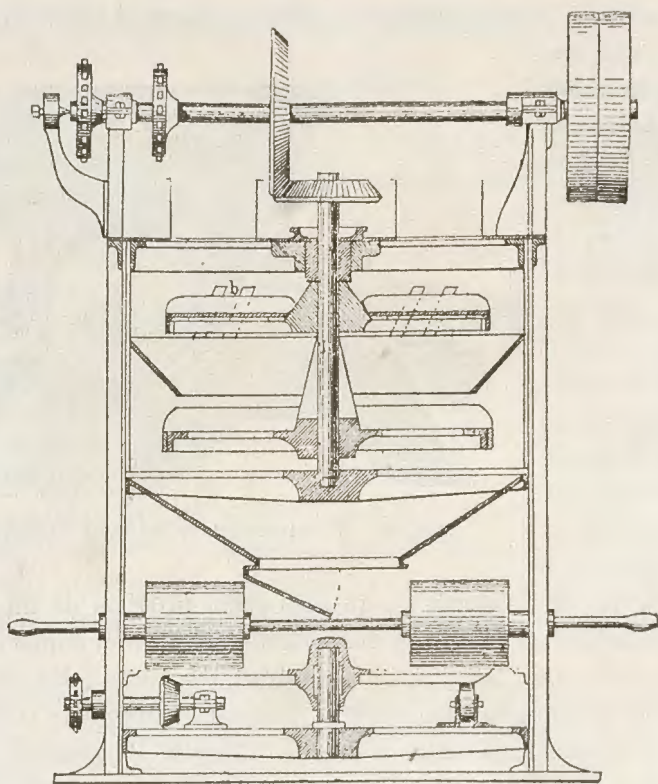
TURBINA AERO-REPELENTE DE M. PAUL
